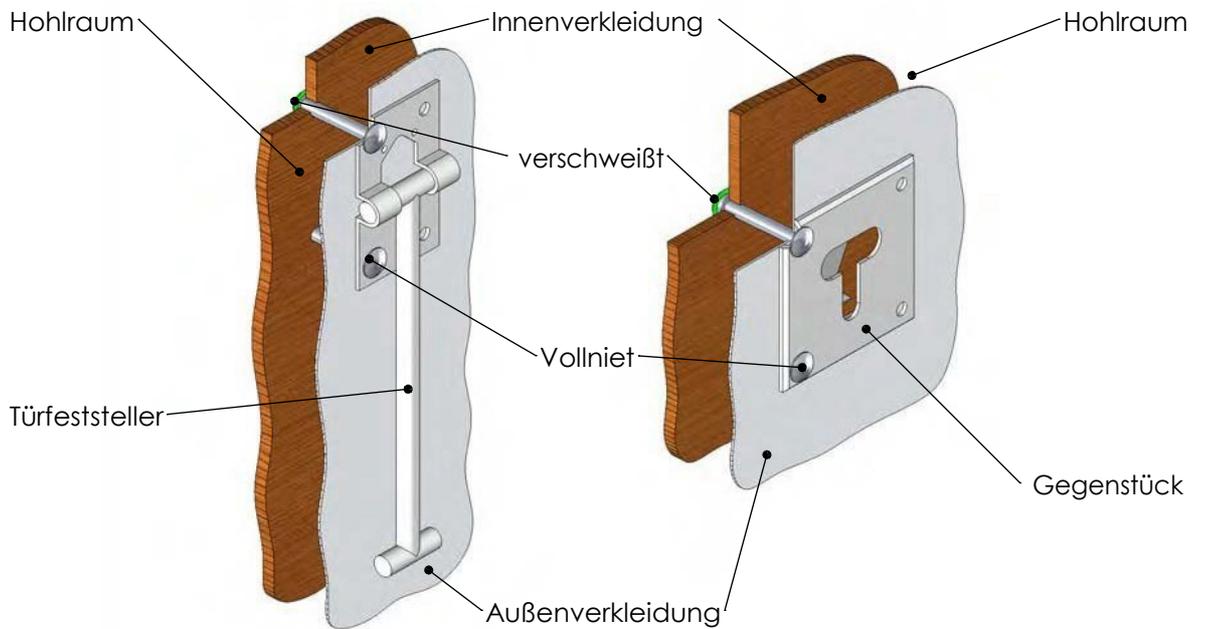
Befestigung mit im Laderaum gesicherten Vollnieten
